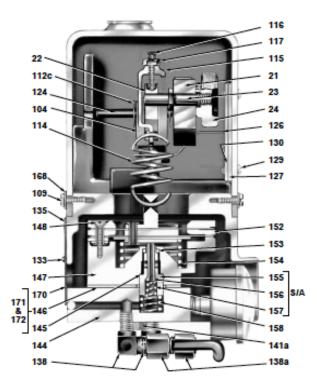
Seção cruzada do atuador VariPak 28002 Cv Regulável e posicionador 7700P
